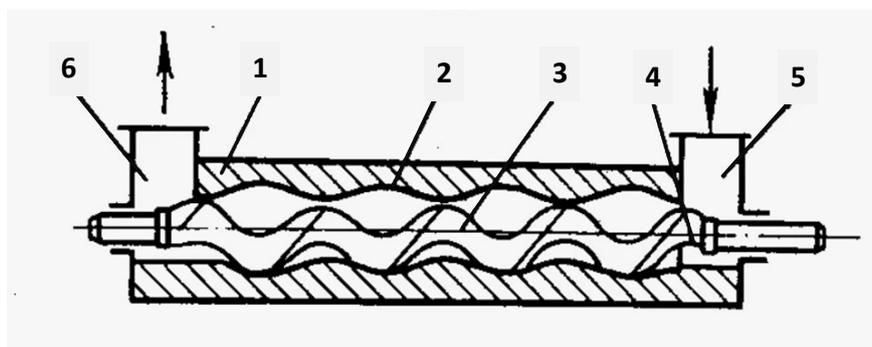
Винтовой насос: 1 – корпус насоса; 2 – цилиндр; 3 – винт; 4 – шейка винта; 5 – всасывающий патрубков; 6 – нагнетательный патрубков
